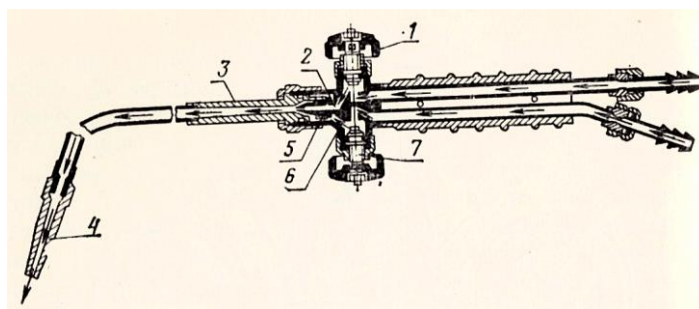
Схема инжекторной горелки для газовой сварки:
